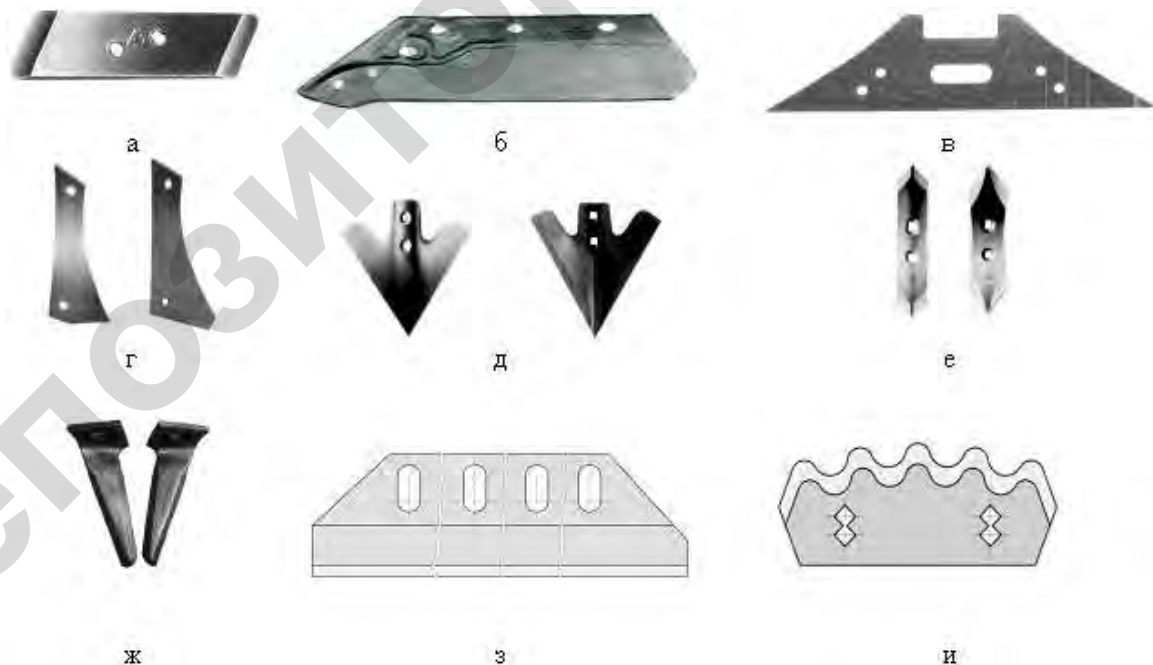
Типовые представители сменных ДРОМ почвообрабатывающих и кормоуборочных машин: а – долото; б – лемех; в – полевая доска; г – груди отвалов; д – стрелчатые лапы; е – оборотные лапы; ж – зубья роторных борон; з – нож измельчающего аппарата кормоуборочного комбайна; и – нож измельчителей рулонов
